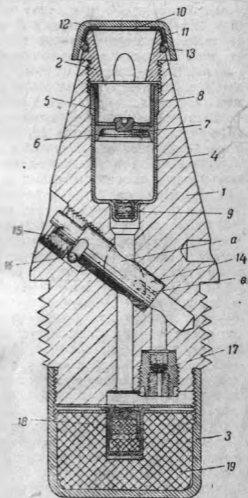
Ударный взрыватель ГВМЗ; 1 — корпус; 2 — головная втулка; 3 — запальный стакан; 4 — гильза; 5 — предохранительная гильза; 6 — обтюратор; 7 — распорная шпилька; 8 — опорное кольцо; 9 — капсюль-воспламенитель; 10 — мембрана; 11 — кольцо; 12 — предохранительный колпачок; 13 — предохранительная втулка; 14 — установочный кран; 15 — гайка крана; 16 — шарик-ограничитель; 17 — пороховой замедлитель; 18 — капсюль-детонатор; 19 — детонатор
